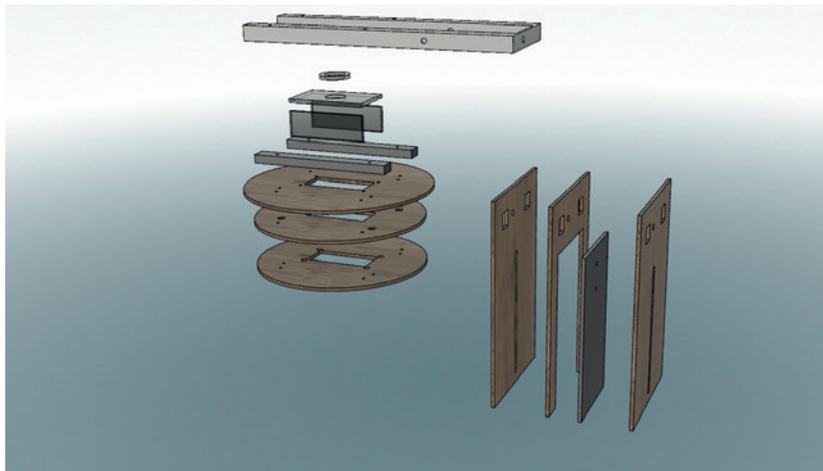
In der Explosionsansicht zeigt sich, dass das Projekt aus sieben Sperrholzteilen, einem Stahl- oder Aluschweißteil und etwas Plexiglas besteht.
